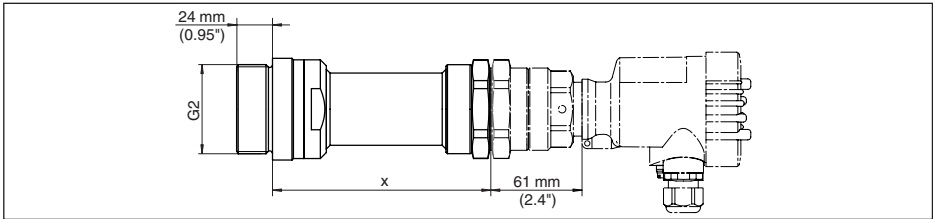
Montageadapter mit Keramikabdeckung (optional) für VEGAMIP 61 mit innenliegender Hornantenne, Gewindeausführung G1½ mit PTFE-Abdeckung (auch mit 1½ NPT-Gewinde)
